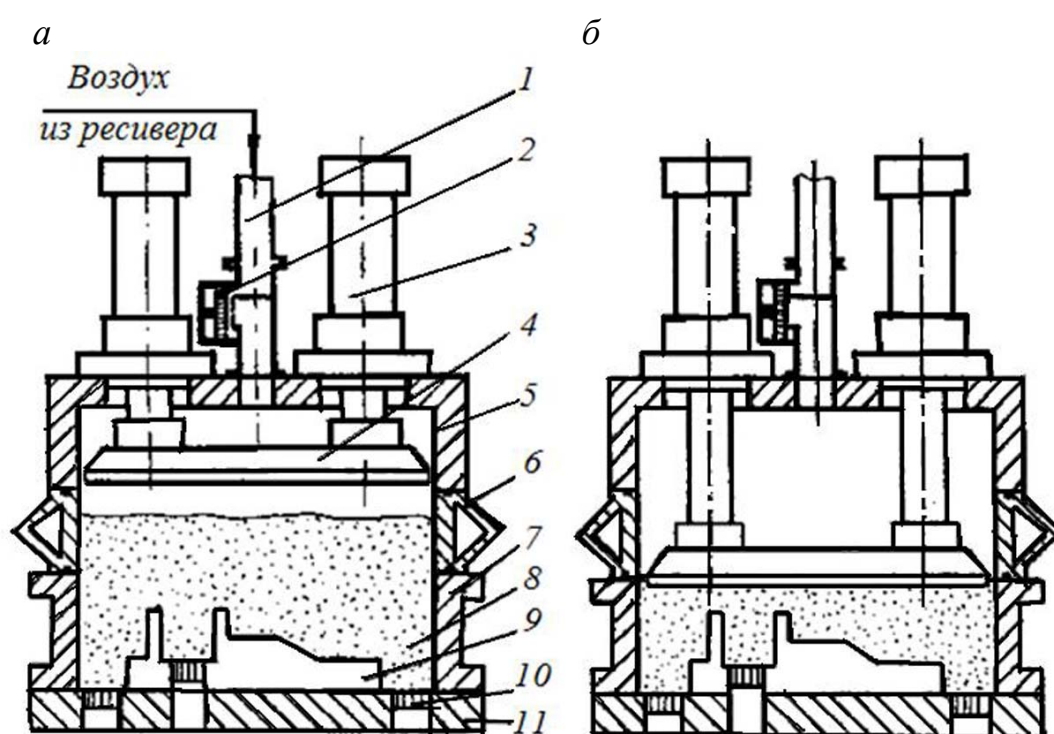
Схема установки для уплотнения форм воздушным потоком с допрессовкой:
